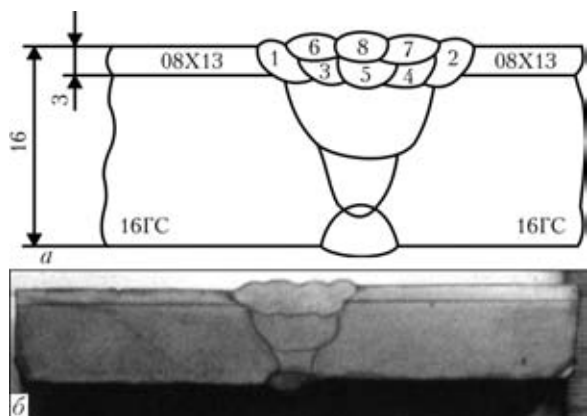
Сварной шов с трещиной со стороны плакирующего слоя из стали 16ГC+08X13: а — форма разделки шва в зоне трещин и последовательность наплавки валиков переходного (1-5) и плакирующего (6-8) слоев электродами АНВ-70Б; б — макроструктура металла отремонтированного шва в поперечном сечении
